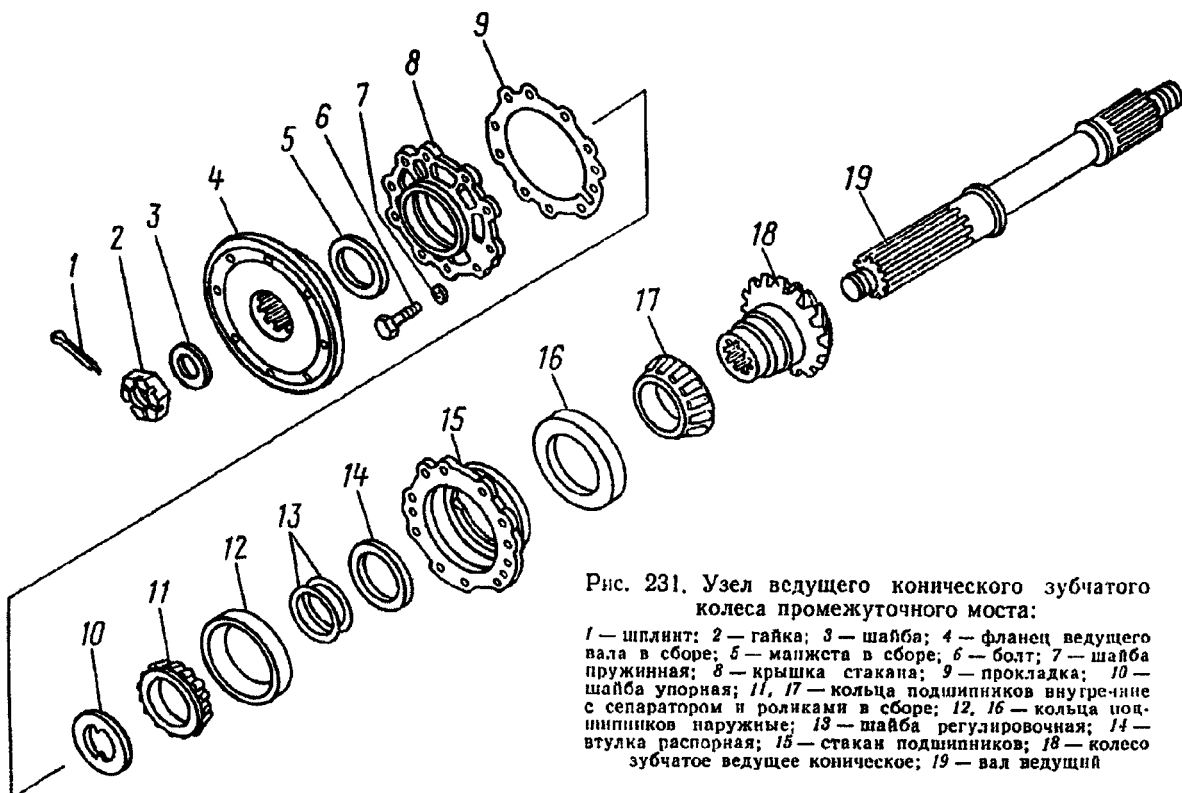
Узел ведущего конического зубчатого колеса промежуточного моста:
